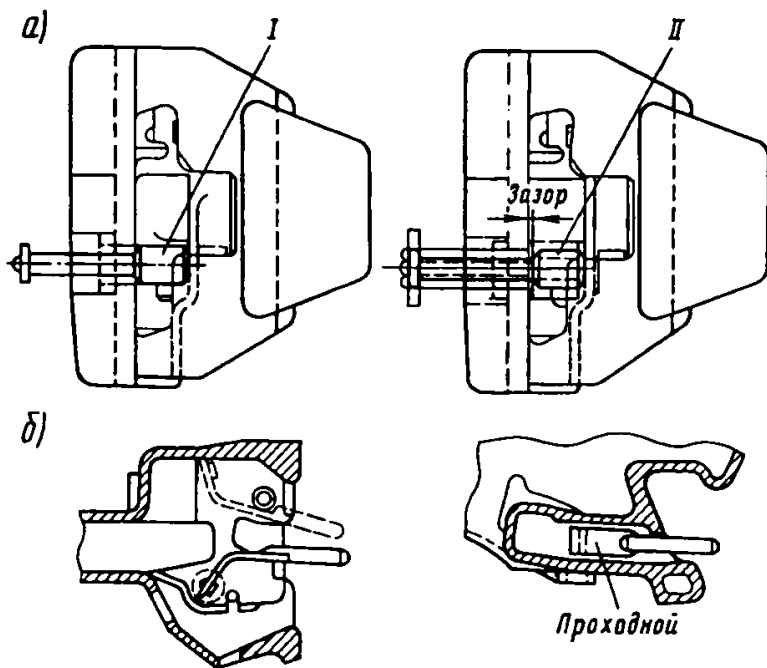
Проверка ширины кармана корпуса автосцепки:
